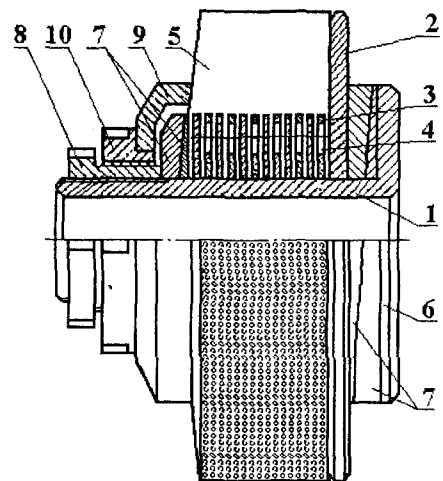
Частичный продольный разрез инструмента с наладкой на нулевой угол наклона режущего и упрочняющего слоя
